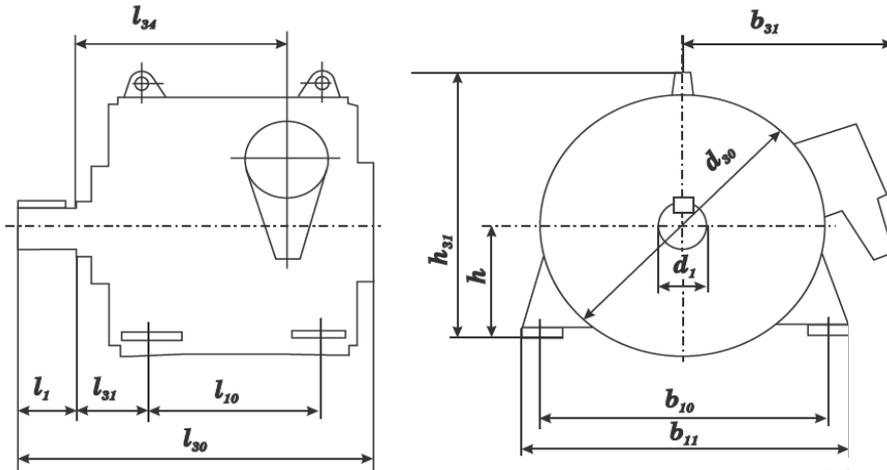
Габаритные, установочные, присоединительные размеры двигателей АКН-4
